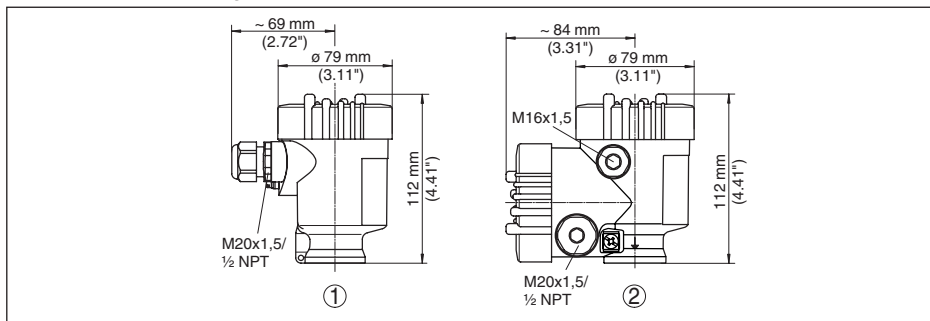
Корпуса в исполнении IP 66/IP 68 (0,2 bar) - с установленным модулем индикации и настройки корпус выше на 9 mm/0.35 in
